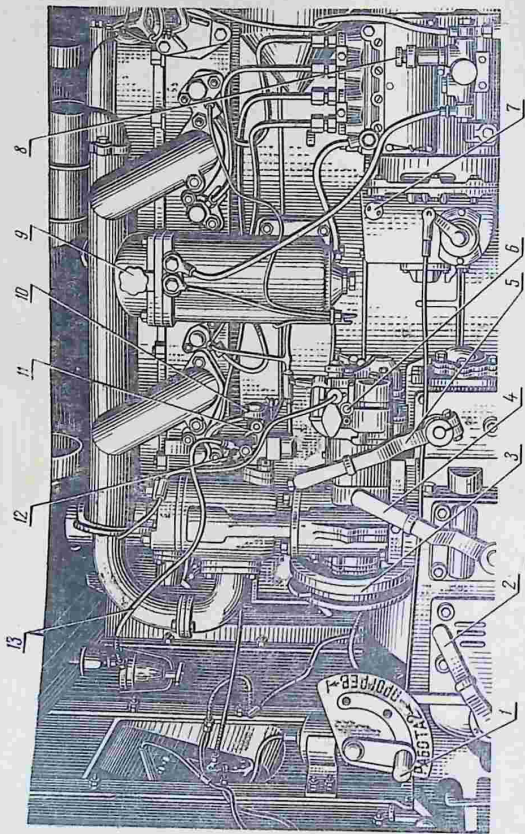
Расположение рычагов управления на двигателе Д-54А:
